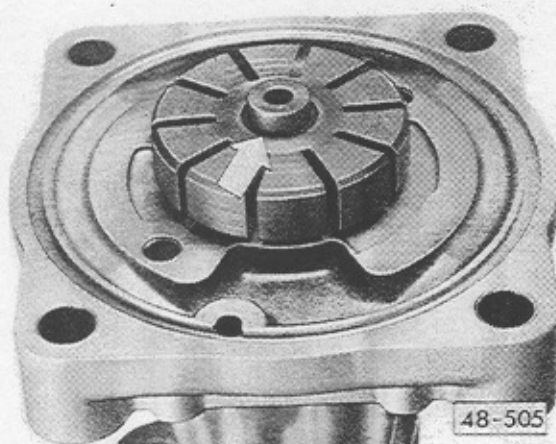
Zum Wechseln des Dichtringes/ Pumpenwelle Rotor und Pumpenwelle ausbauen
